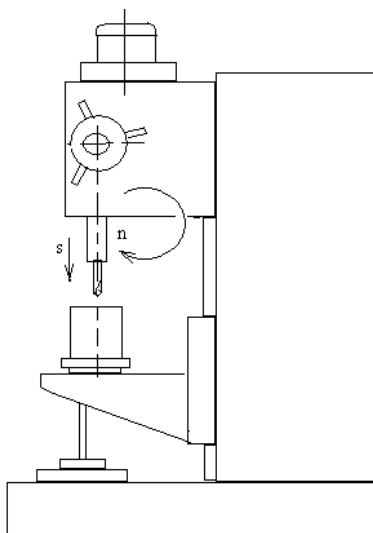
Схема компоновки вертикально-сверльного станка
